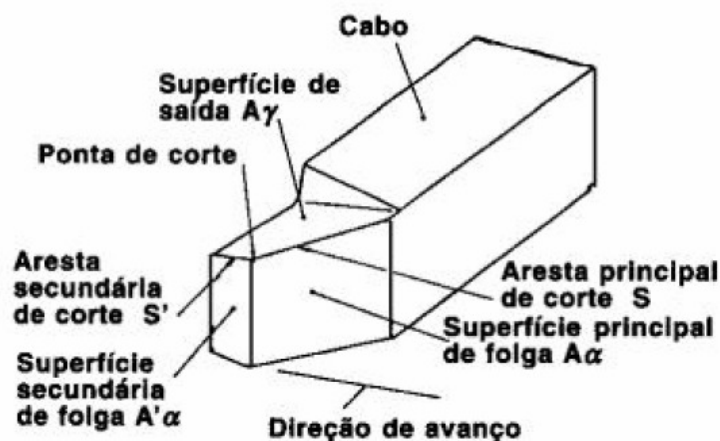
Geometria da ferramenta de corte (Machado e Silva, 1999)
